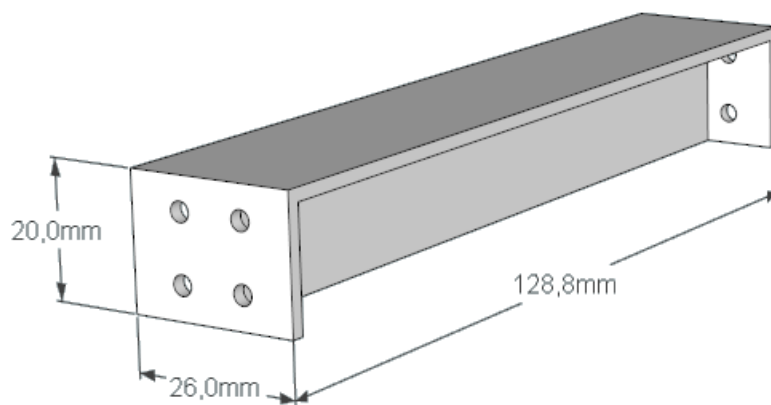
Трёхмерный вид детали 1го звена с указанными размерами
